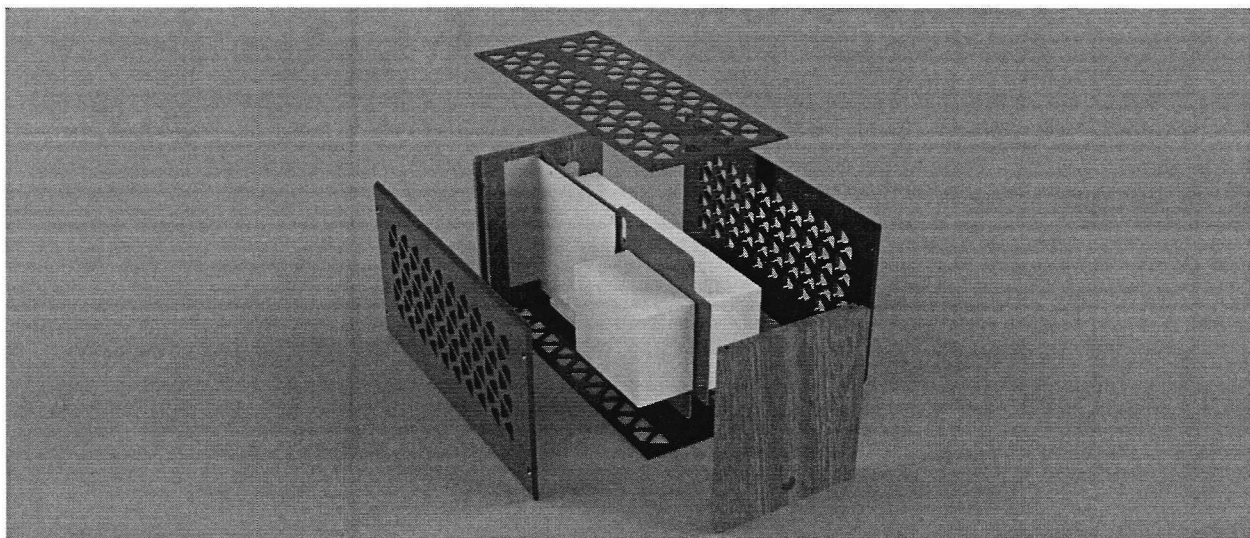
3D модель корпуса (компоновка комплектующих)
